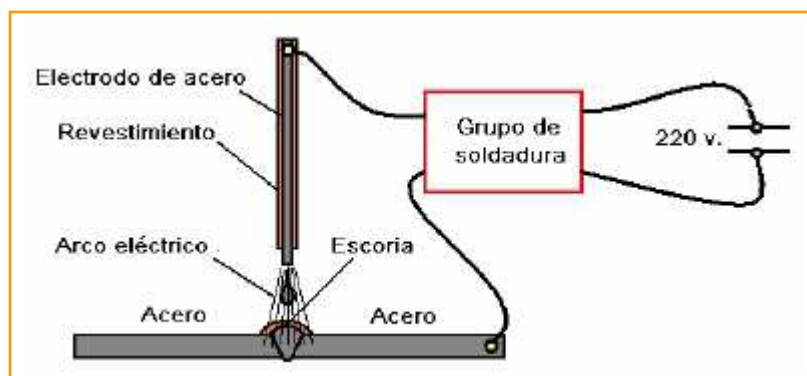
Soldadura por arco manual en electrodos revestidos.
